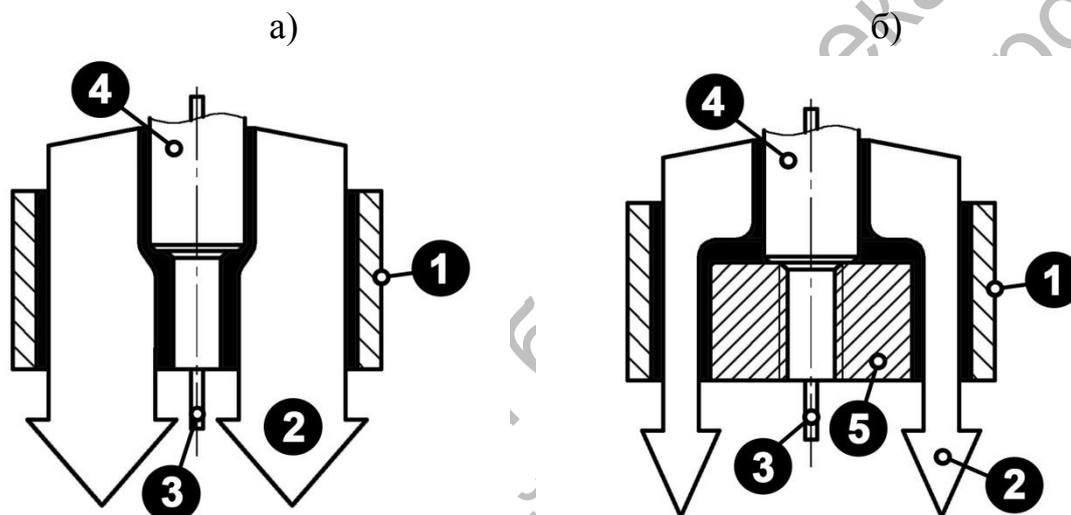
Схемы подачи защитного газа в зону сварки при традиционном и комбинированном способе газовой защиты: а – схема с традиционной подачей защитного газа в зону сварки; б – схема с кольцевой подачей защитного газа; 1 – сопло сварочной горелки; 2 – поток защитного газа (CO_2); 3 – электродная проволока; 4 – токоподводящий наконечник; 5 – втулка для распределения газового потока
